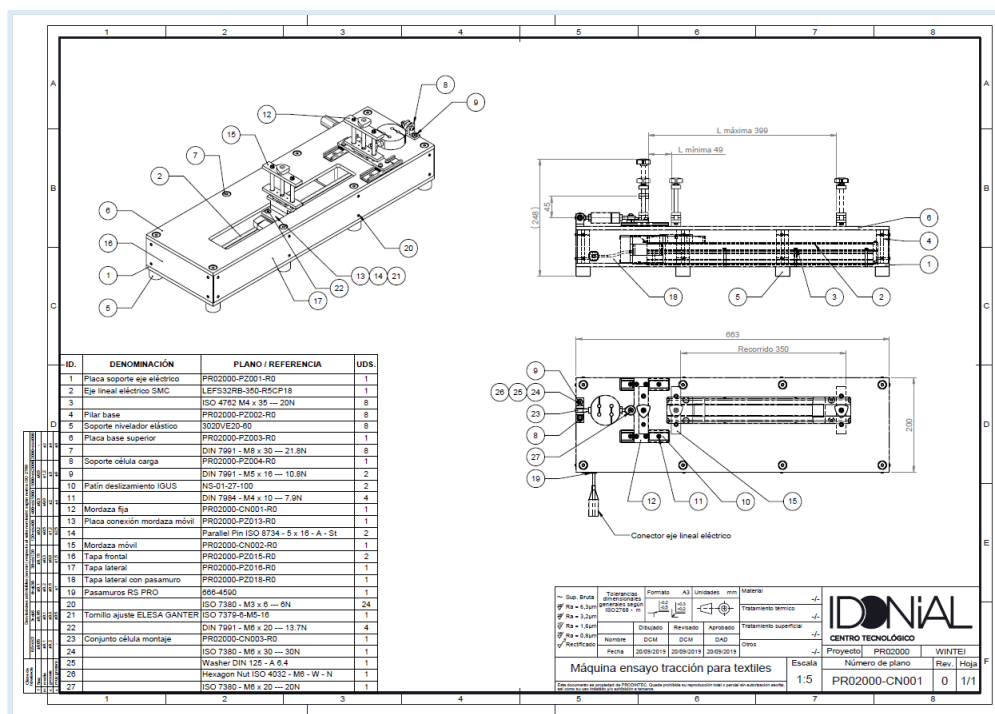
Plano de conjunto del equipo diseñado para ensayos mecánicos
